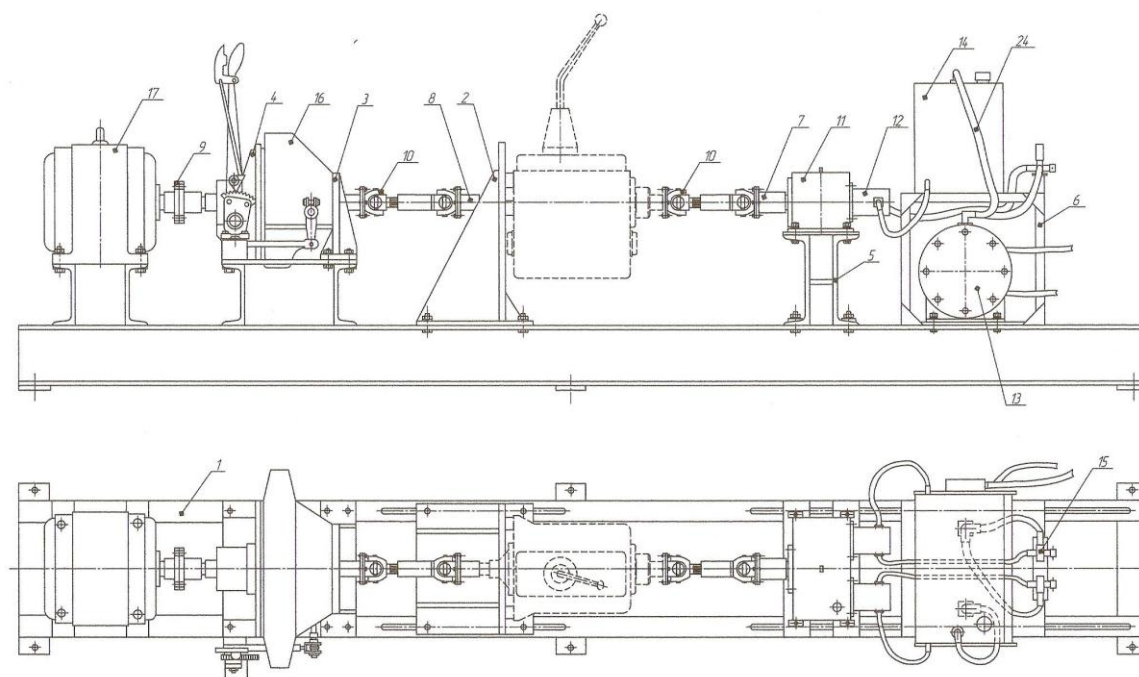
Стенд обкатки КПП собственной конструкции
